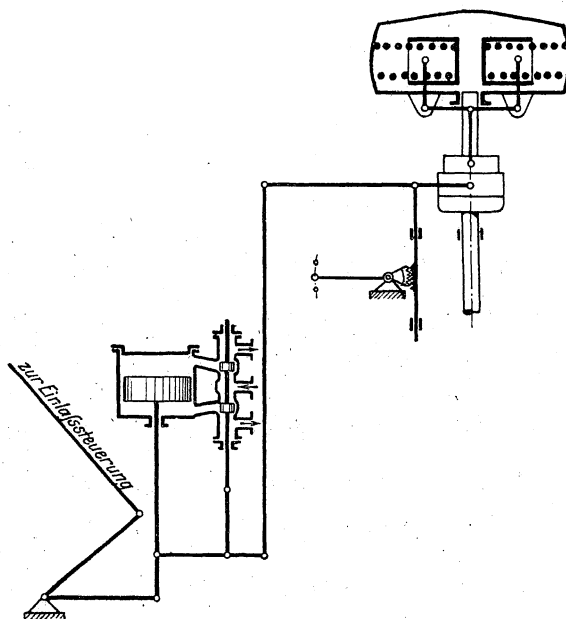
Steuerregelung der Gasmaschinen V und VI.
